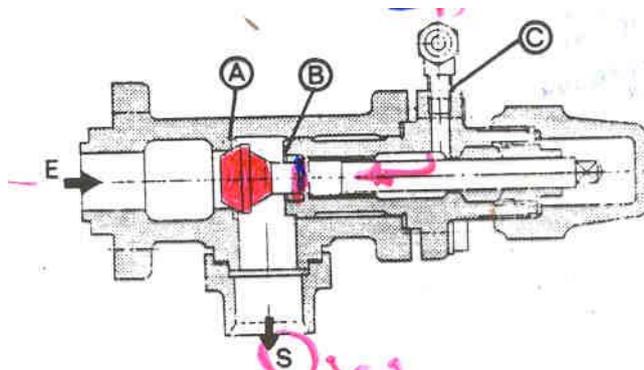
VÁLVULA DE INSPEÇÃO
